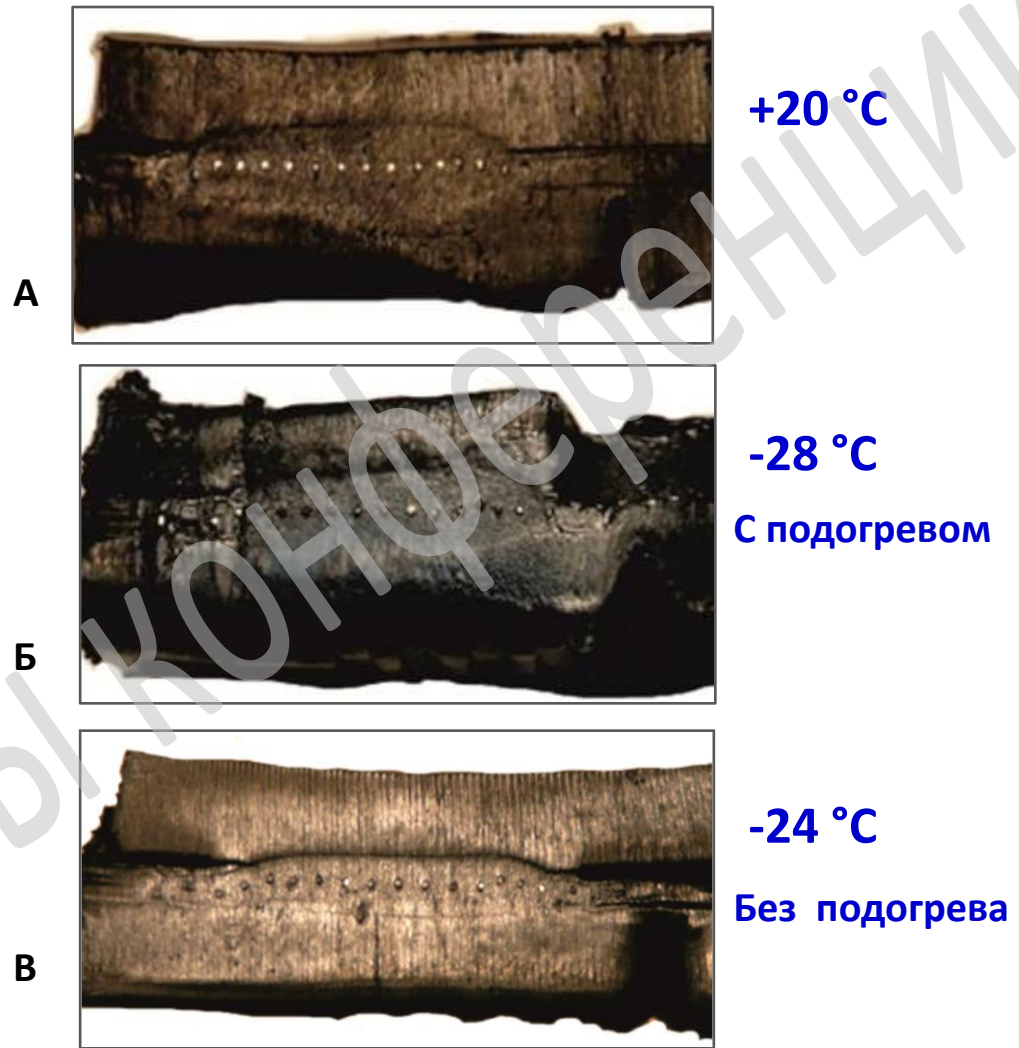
Область расплава муфтовых сварных соединения после локального вторичного нагрева:
